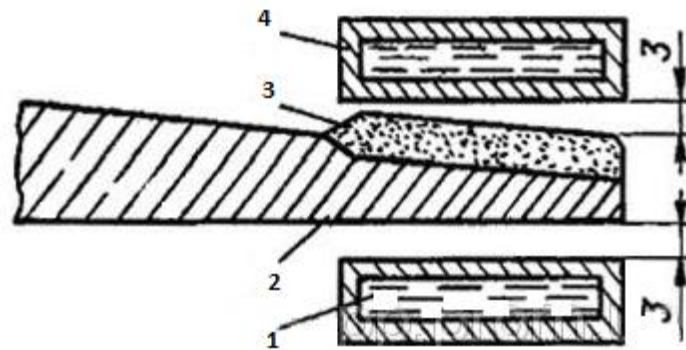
Схема індукційного наплавлення порошковим матеріалом:
